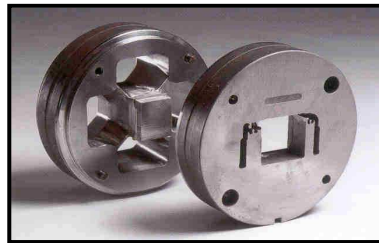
Werkzeug für Hohlprofile [Quelle: Hydro]
